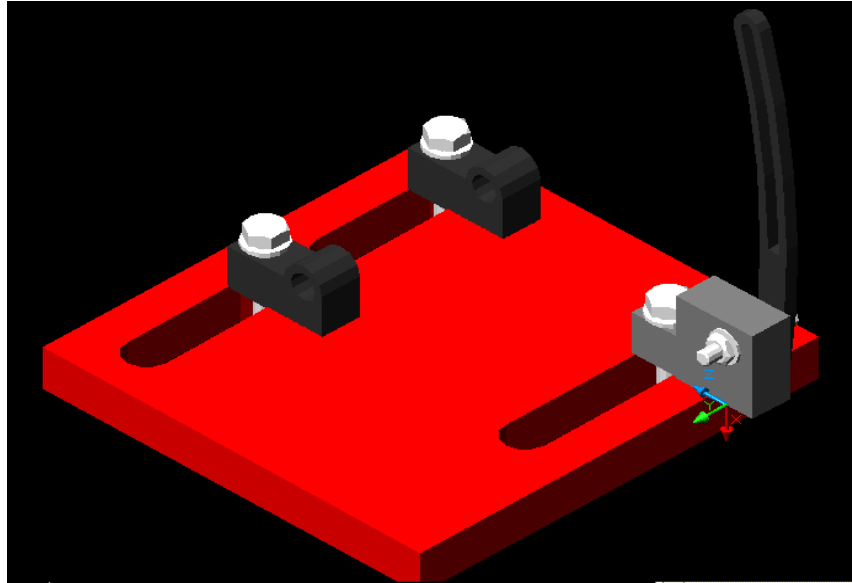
Vista isométrica 2 de la placa que soporta el alternador
